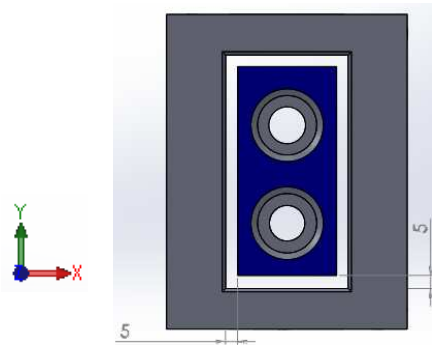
Spojení upínacího mechanismu s deskou stolu
